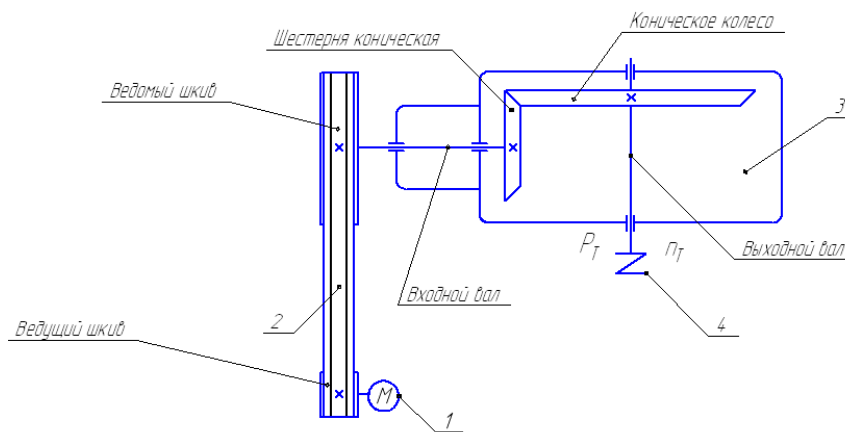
Кинематическая схема привода с коническим редуктором
